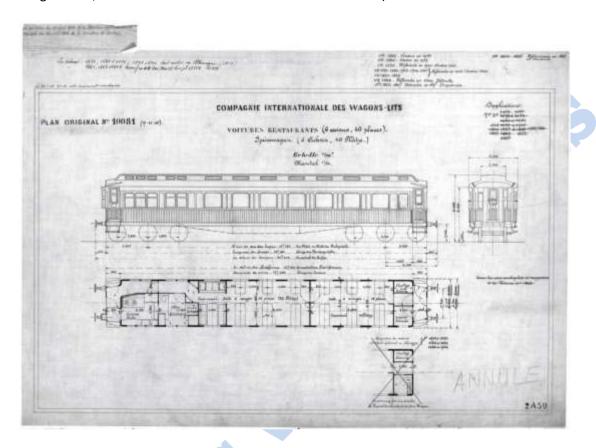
Plan N°. 10081, Scan vom Plan: Eisenbahnmuseum Strasshof
